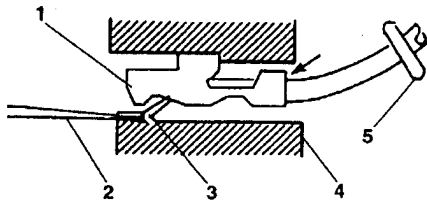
Типовой герметизированный соединитель: 1 - корпус соединителя; 2 - контакт; 3 - уплотнитель; 4 - фиксирующий язычок; 5 - инструмент для извлечения контактов
